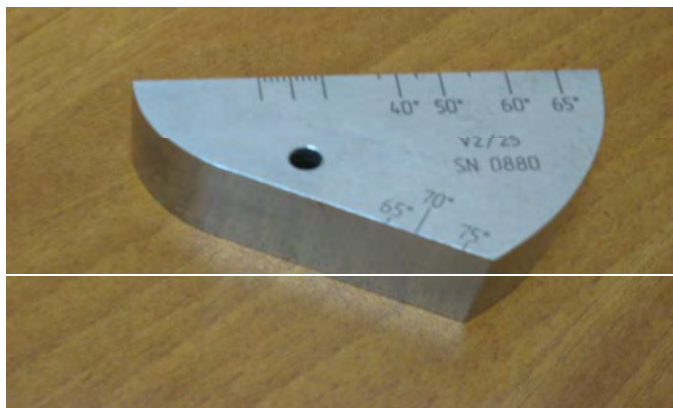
Общий вид калибровочного ультразвукового образца V2/25
